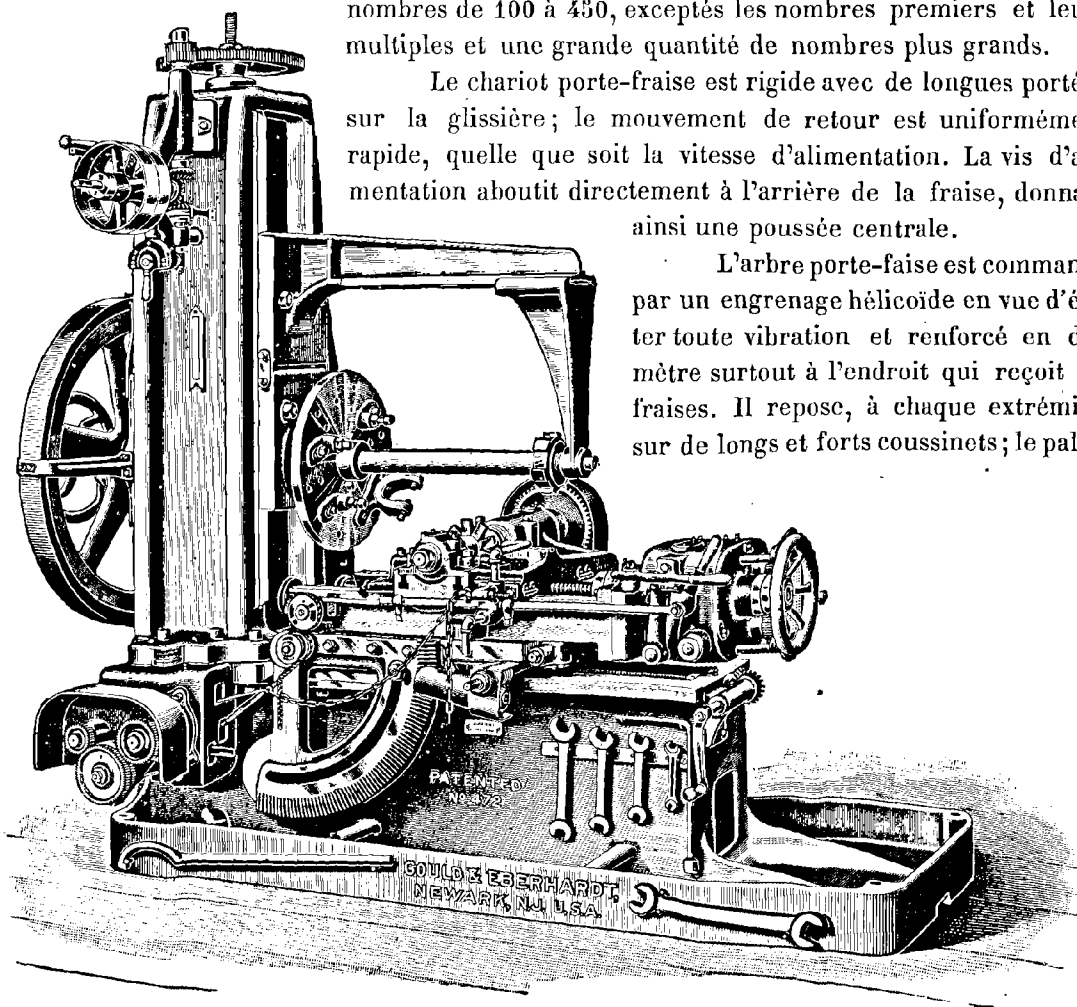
Machine automatique à tailler les engrenages de Gould et Eberhardt.
